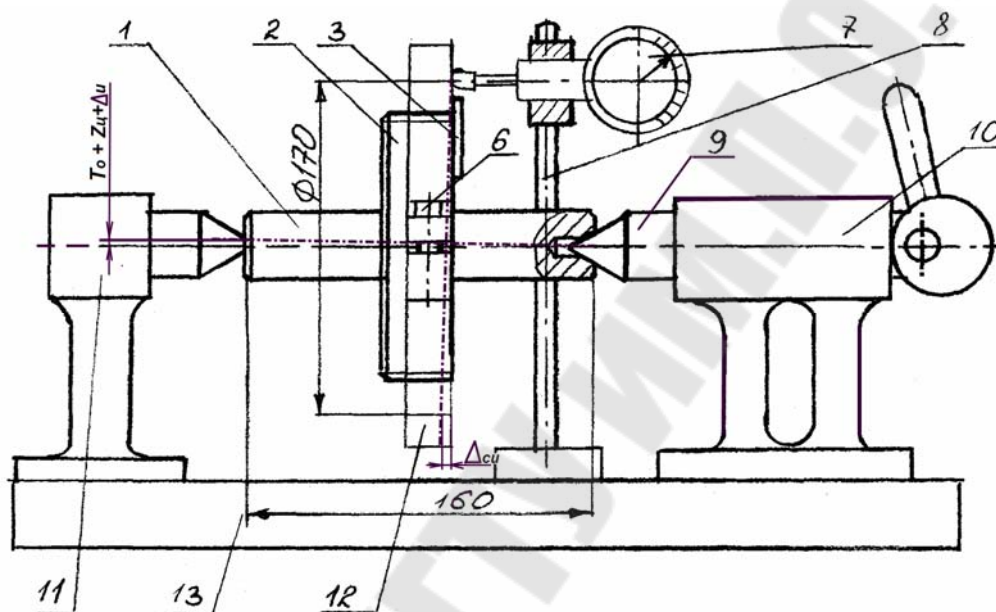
Приспособление для контроля торцового биения гайки регулировочной
